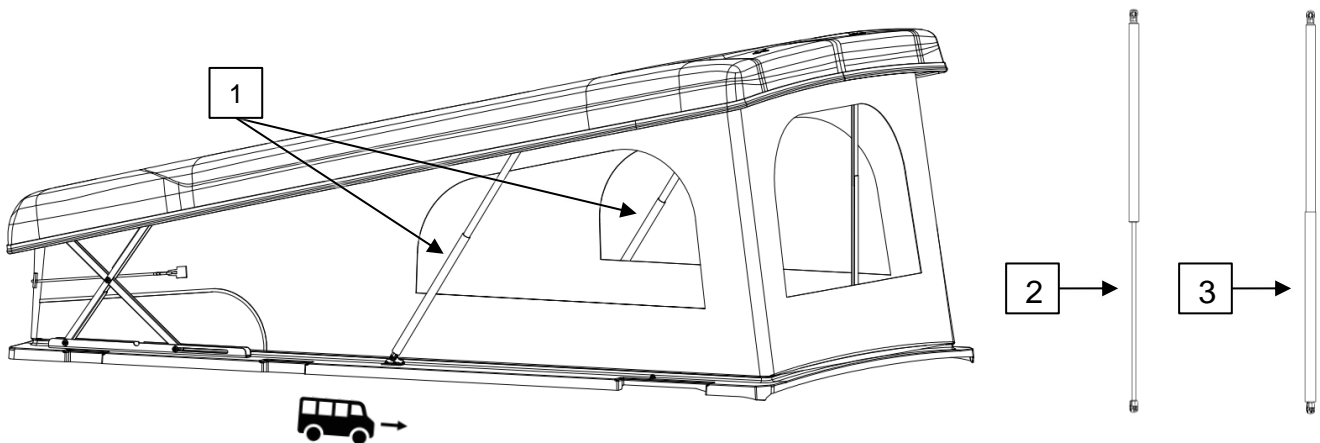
Außenansicht Schlafdach / Exterior view pop top roof [G0001549]
